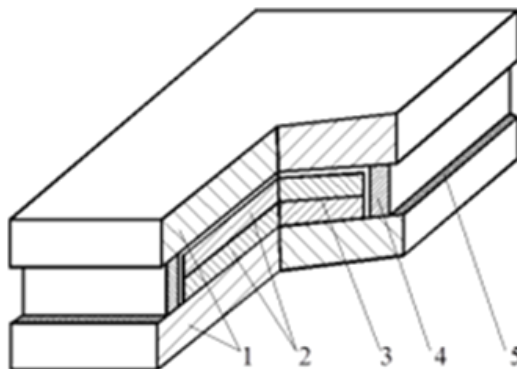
Конструкція чотиришарового біметалічного пакета. 1 – основні шари; 2 – плакуючі шари; 3 – розділовий шар; 4 – сполучна планка; 5 – зварений шов [13]
